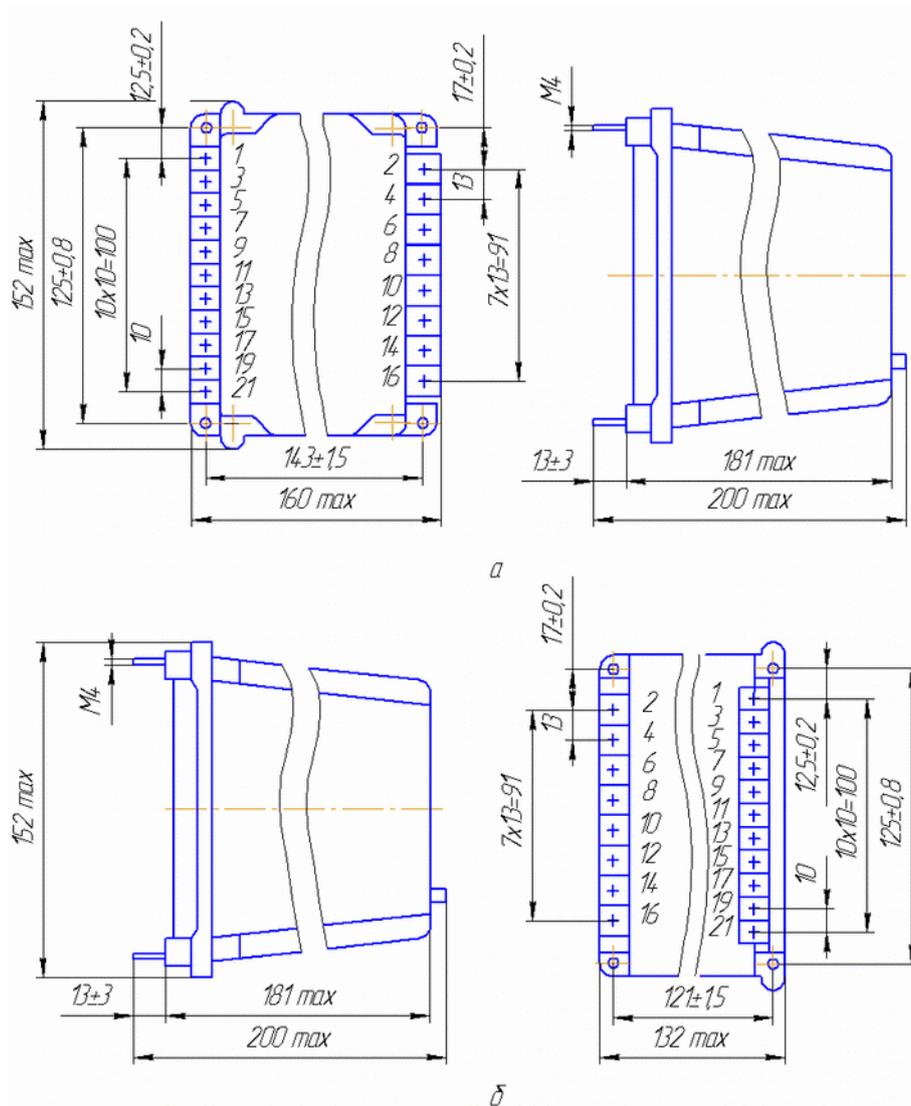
Габаритные, установочные, присоединительные размеры защиты типа 33Н
